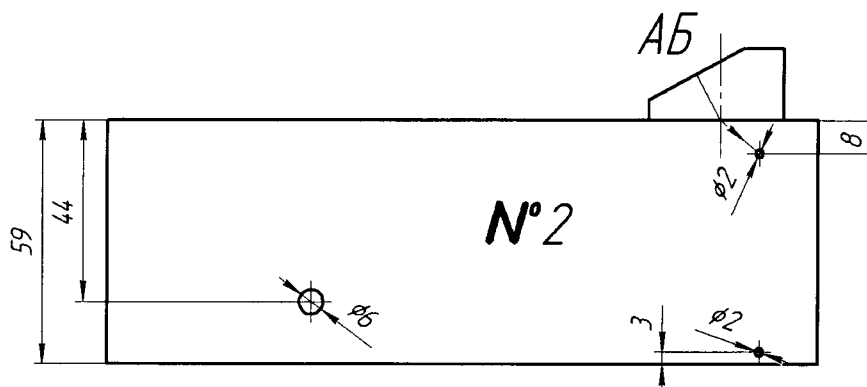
Установка акустического блока на поверхность контрольного образца №2 для получения сигнала от бокового сверления диаметром 2 мм на глубине 8 мм.
